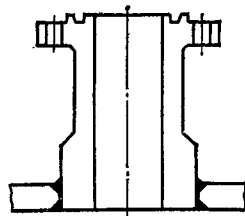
Самоусиливающийся патрубок с длинной сварной шейкой
